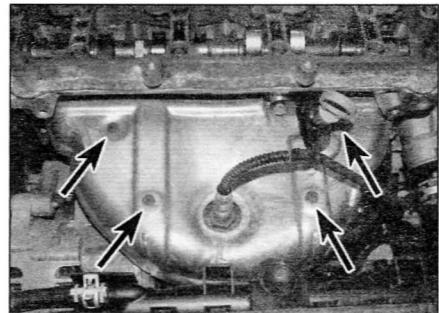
Выверните болты (отмечены стрелками) и снимите кожух с верхней части выпускного коллектора
